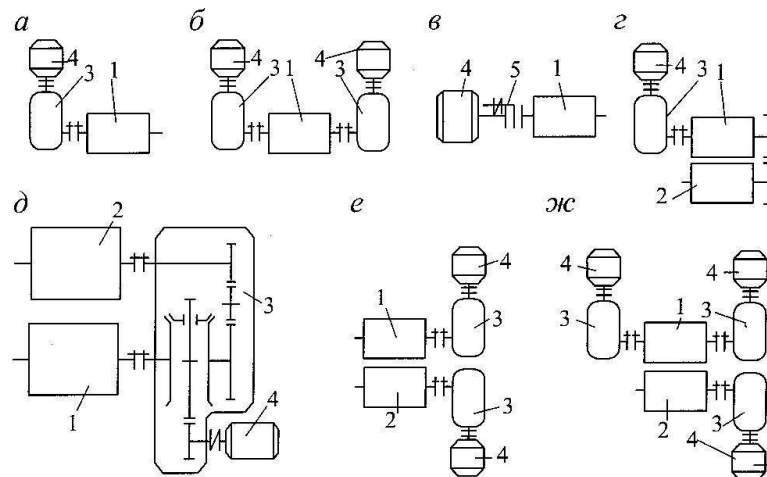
Схеми привідних станцій: а, б, в – однобарабанні; г, д, е, ж – двобарабанні; 1,2 – барабани; 3 – редуктор; 4 – двигун; 5 – муфта
